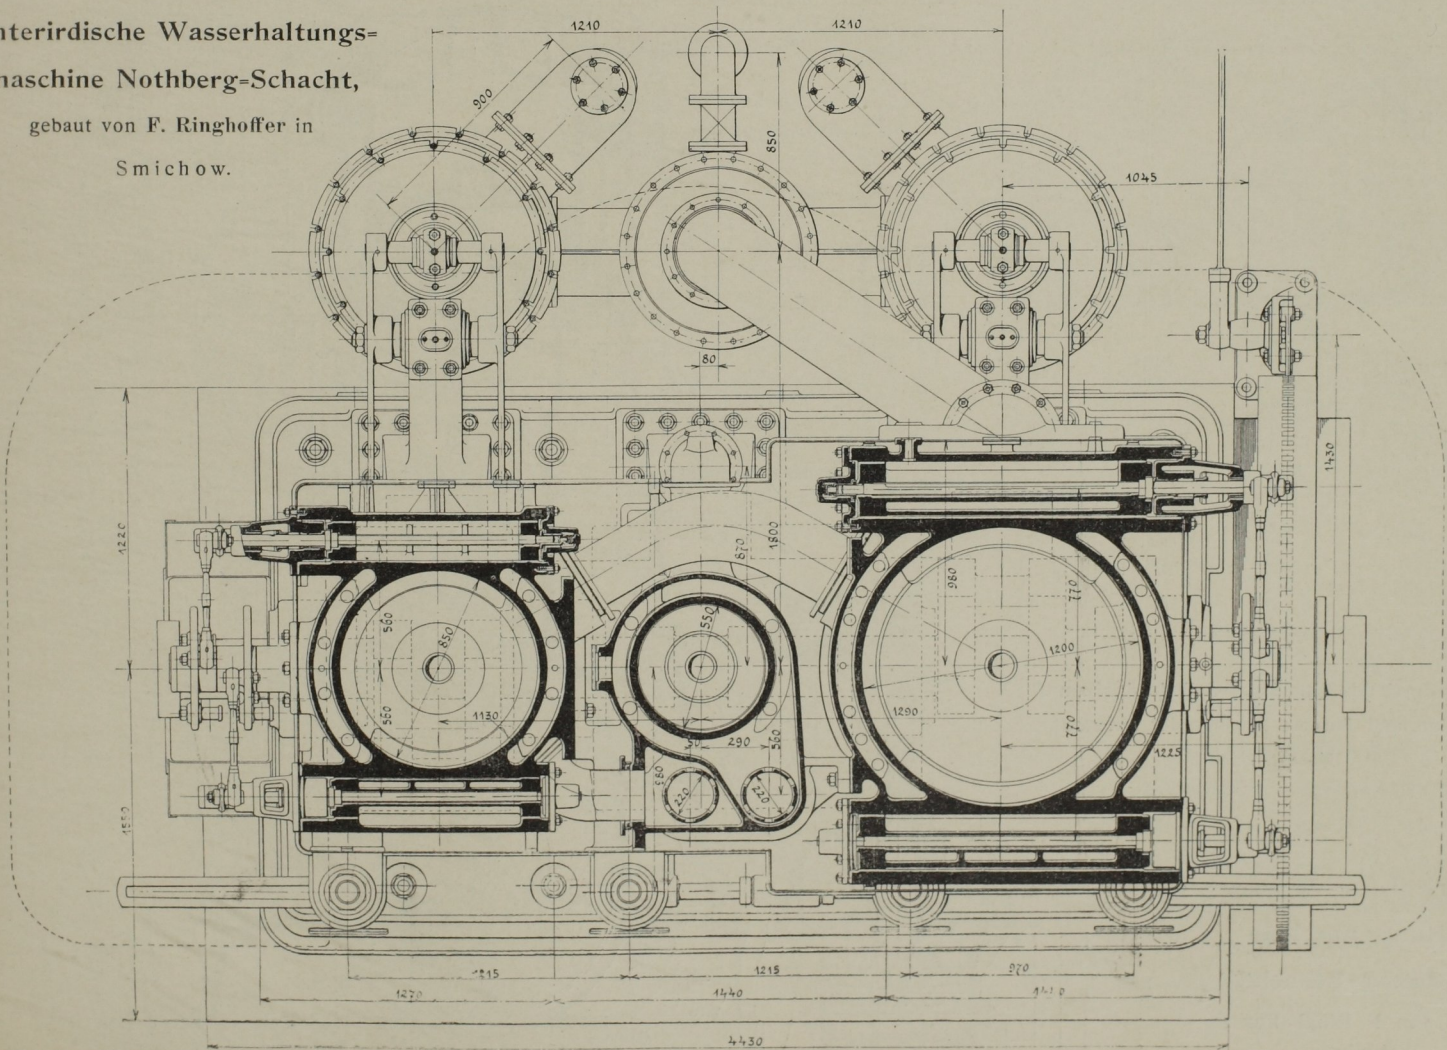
Grundriss der Dampfmaschine. Masst 1:30.
